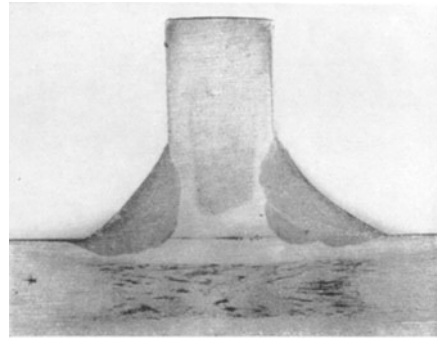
Gute elektrische Kehlnaht-Schweißungen. ( $V = 1$ ).
